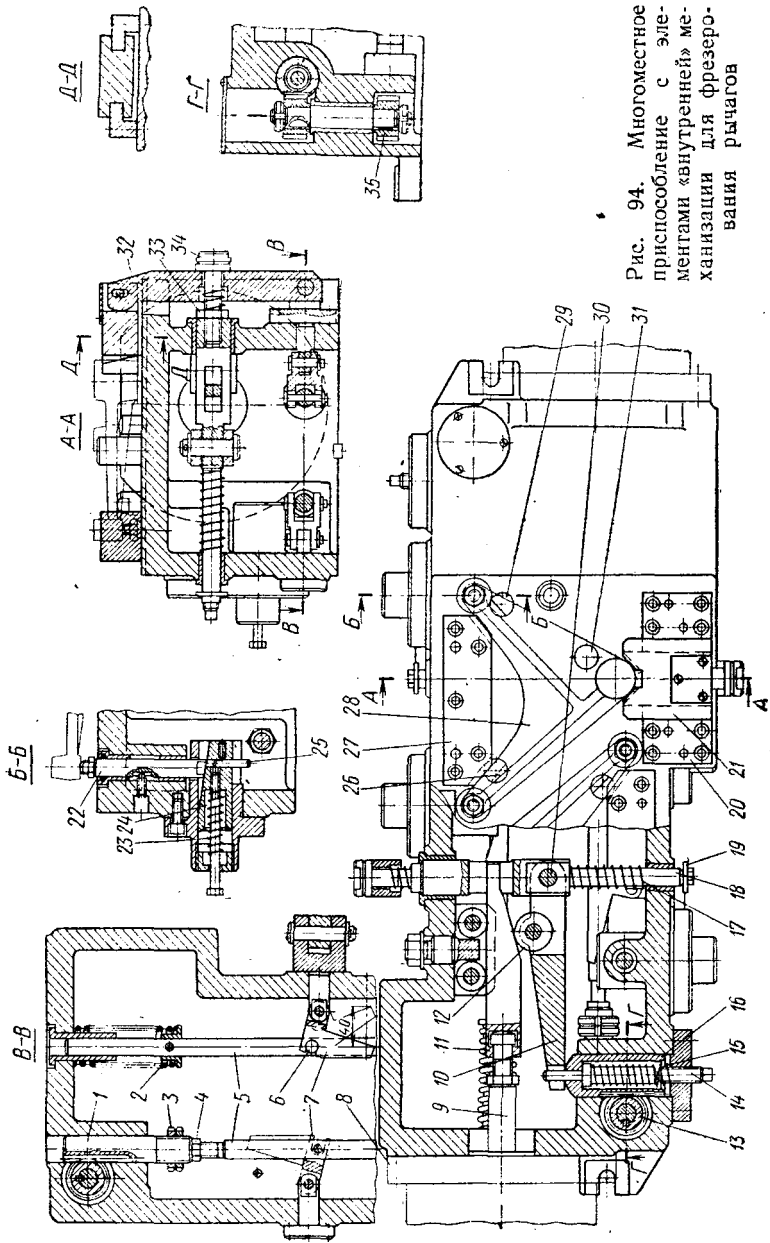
Многоместное приспособление с элементами «внутренней» механизации для фрезерования рычагов
